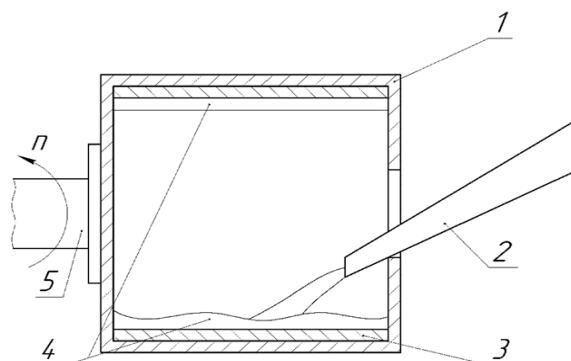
Процесс разлива стали в изложницу установки центробежного литья:
